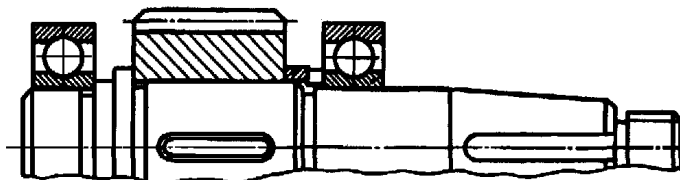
Вал цилиндрической передачи в сборе с шестерней и подшипниками качения
